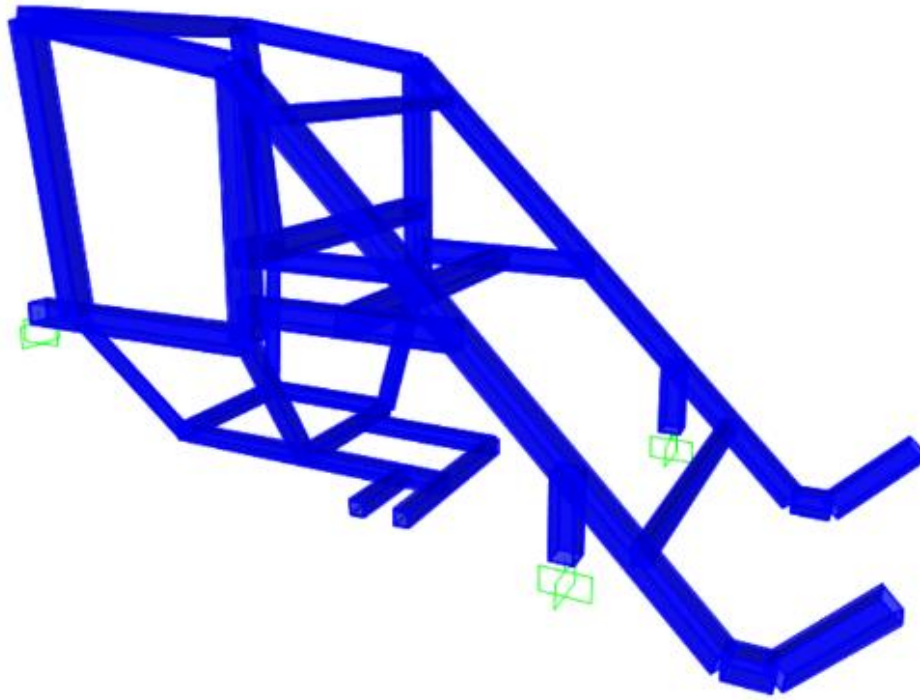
Modelado de la estructura con elementos tipo frame. Fuente: SAP2000, 2019.
